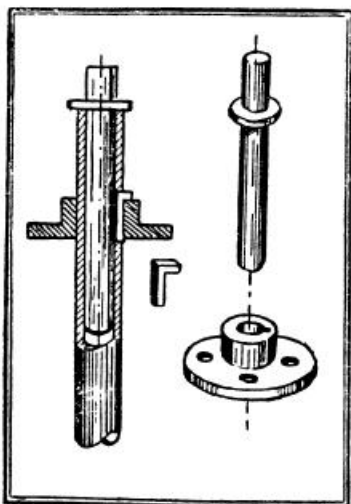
Способ крепления на трубчатом валу шипа (цапфы) шпонки металлического фланца для диска гидроротора
